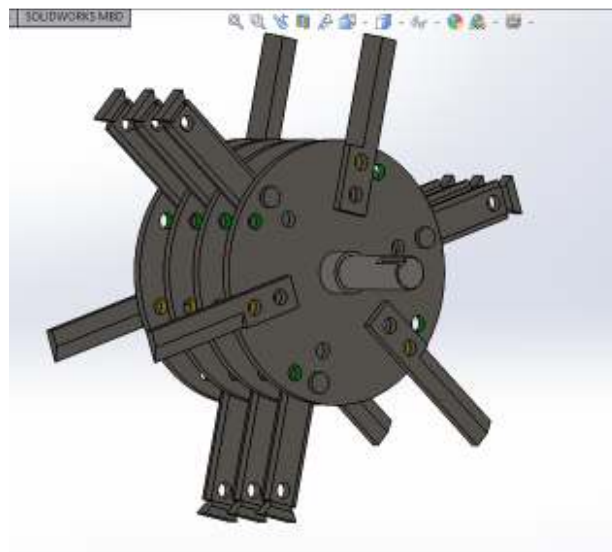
Ensamblaje de elementos internos o de corte del equipo mecánico (15 martillos).
